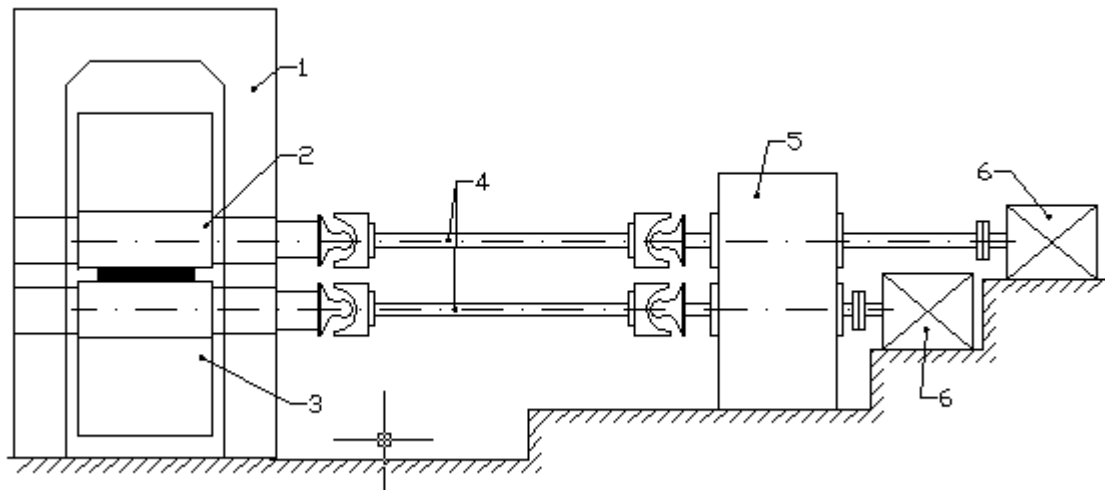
Схема рабочей клетки стана: 1 – станина; 2 – рабочие валки; 3 – опорные валки; 4 – универсальные шпиндели; 5 – комбинированный редуктор; 6 – электродвигатели
